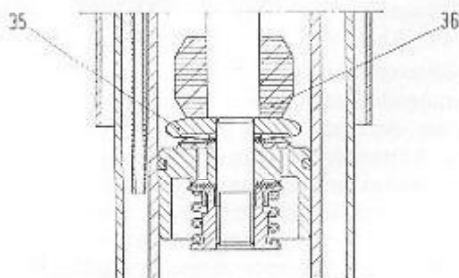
Teilquerschnitt durch einen hinteren hydr. Stossdämpfer.
